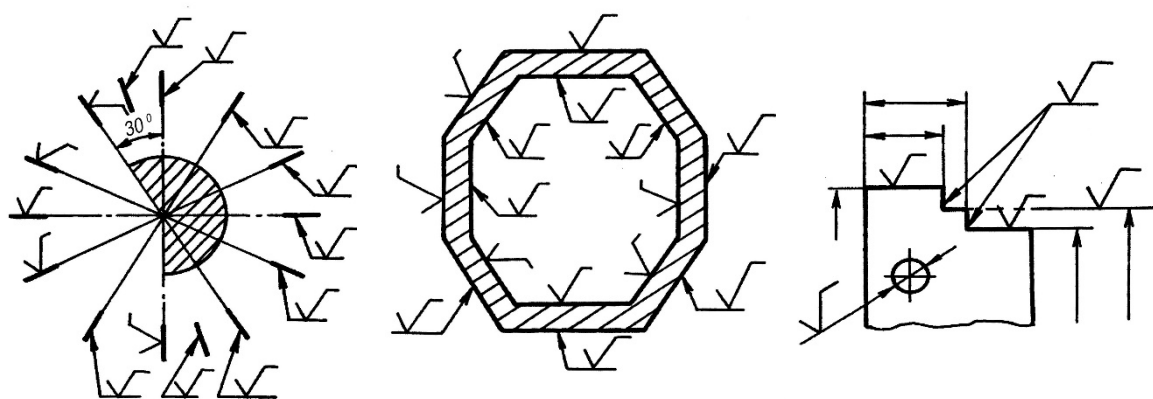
Расположение знаков шероховатости на изображениях чертежа
